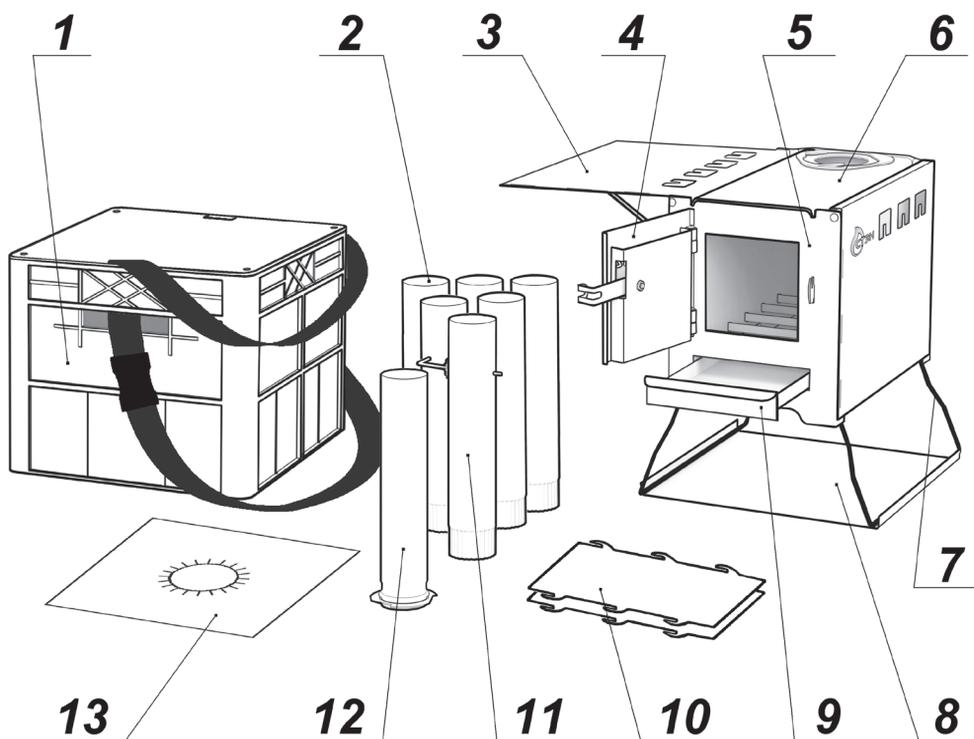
Комплектация печи: 1 – ящик транспортировочный с крышкой и ремнём; 2 – труба \varnothing 65; 3 – экран-столик; 4 – дверца загрузочная; 5 – корпус; 6 – варочная панель; 7 – складная ножка; 8 – металлический лист; 9 – зольный ящик; 10 – бортик каменки; 11 – труба \varnothing 65 с шибером; 12 – труба \varnothing 65 с фланцем; 13 – проход потолочный.
